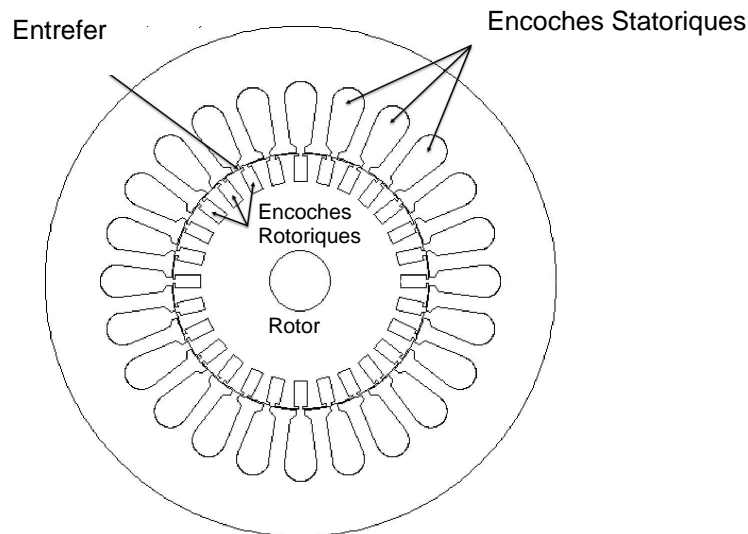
Configuration géométrique de la machine asynchrone
